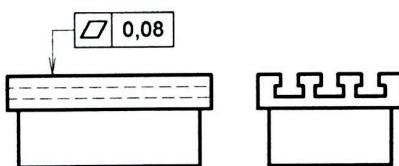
, Predpis tolerancie priamosti,
